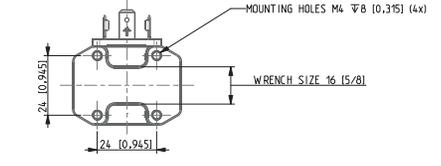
Dimensiones 1/4" en línea, ancho de bobina 32 mm
